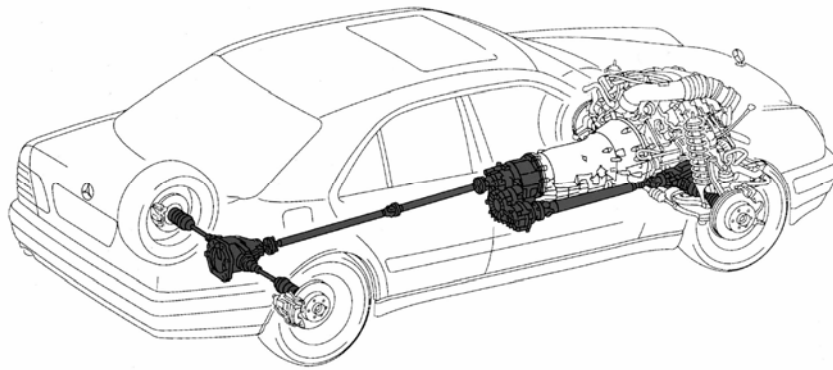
Front engine and four-wheel-drive: motore anteriore, 4 ruote motrici, sospensioni indipendenti.
